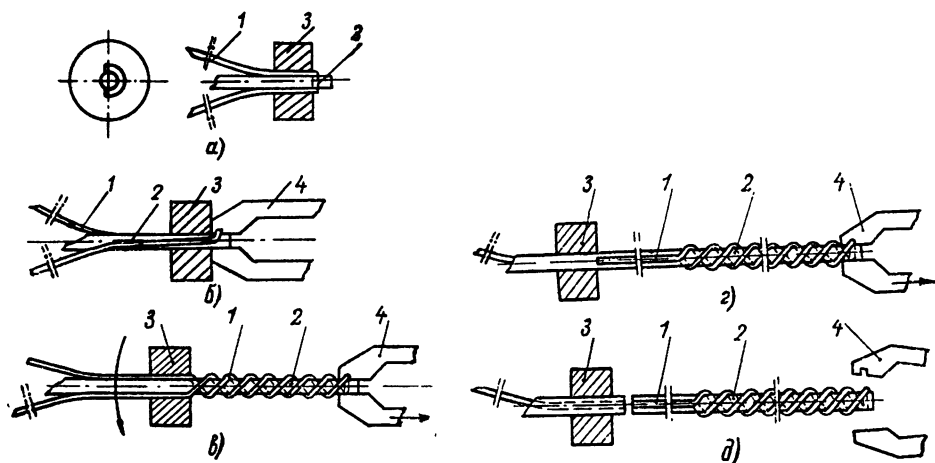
Последовательность изготовления бифилярной спирали на непрерывном керне:
